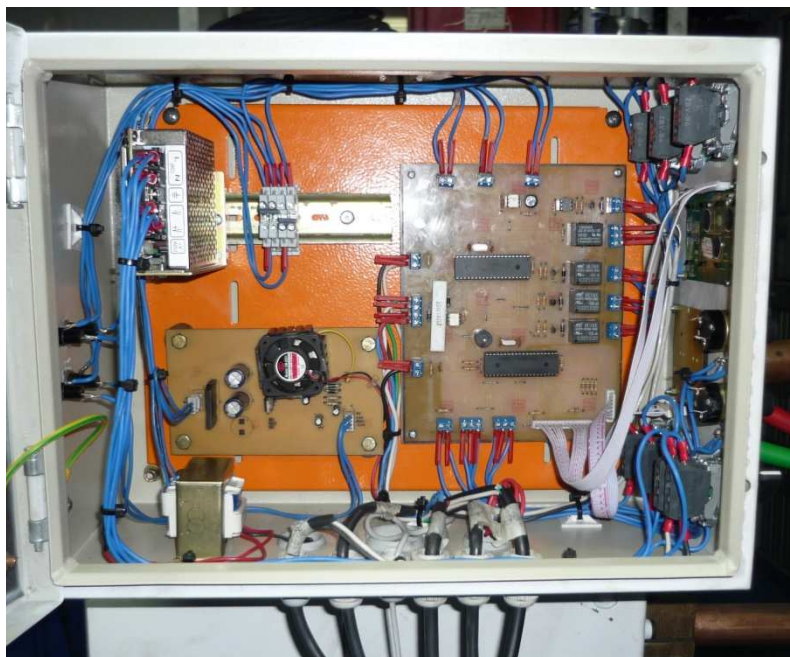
Tarjeta principal instalada en la soldadora de resistencia por puntos
